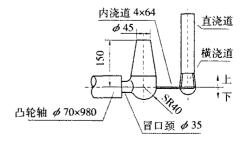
6110凸轮轴的浇注系统和锥形冒口(每型6件) Fig.15 Gating system and tapered feeder for 6110 camshaft (6 pcs/per mould)
